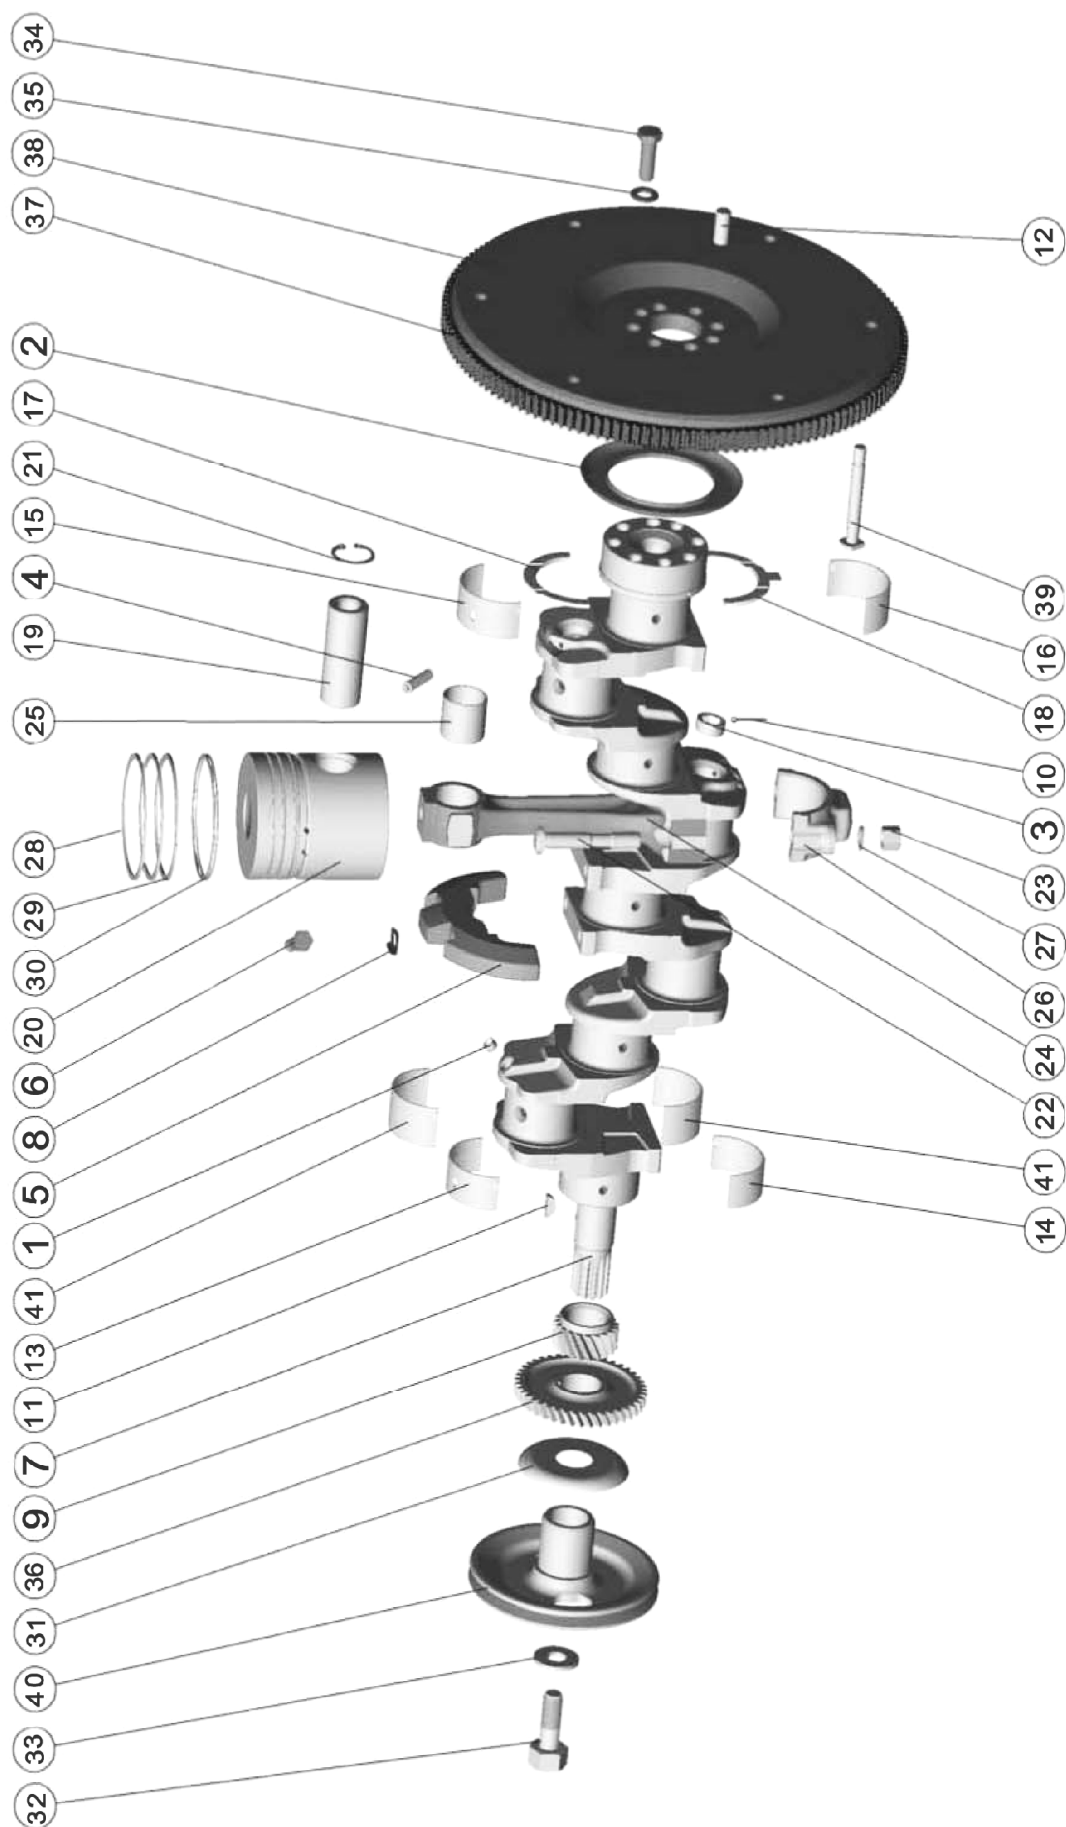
Поршни и шатуны. Коленчатый вал. Маховик
